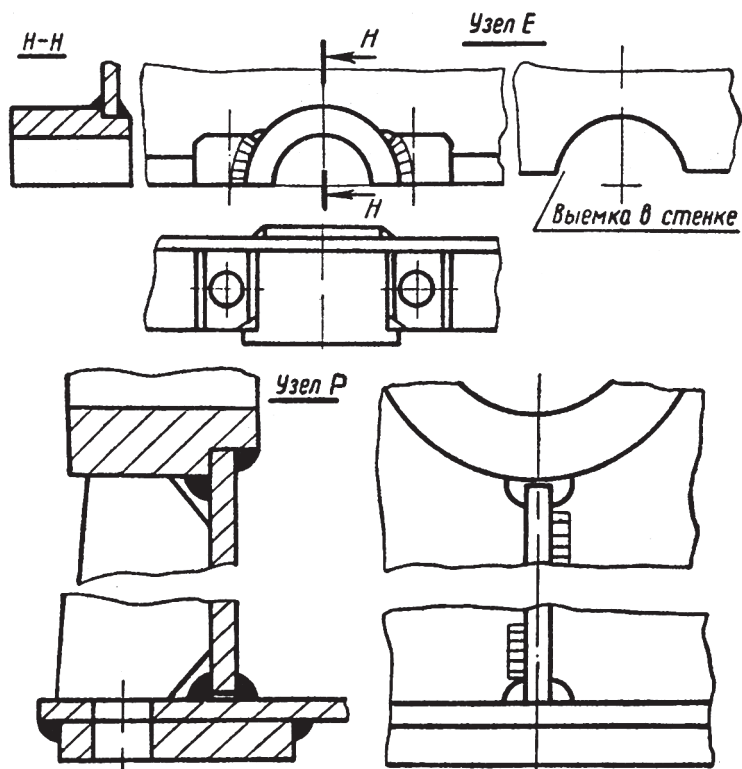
Конструктивные элементы для сопряжения стенок, фланца и бобышки
